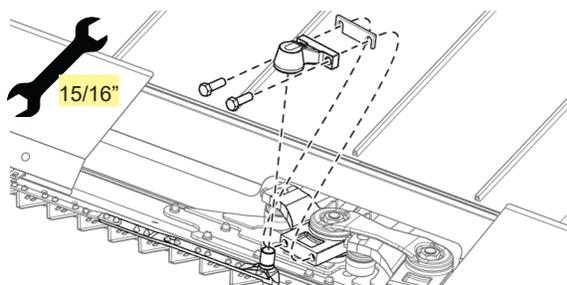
Снятие корпуса подшипников с головки правого ножа
